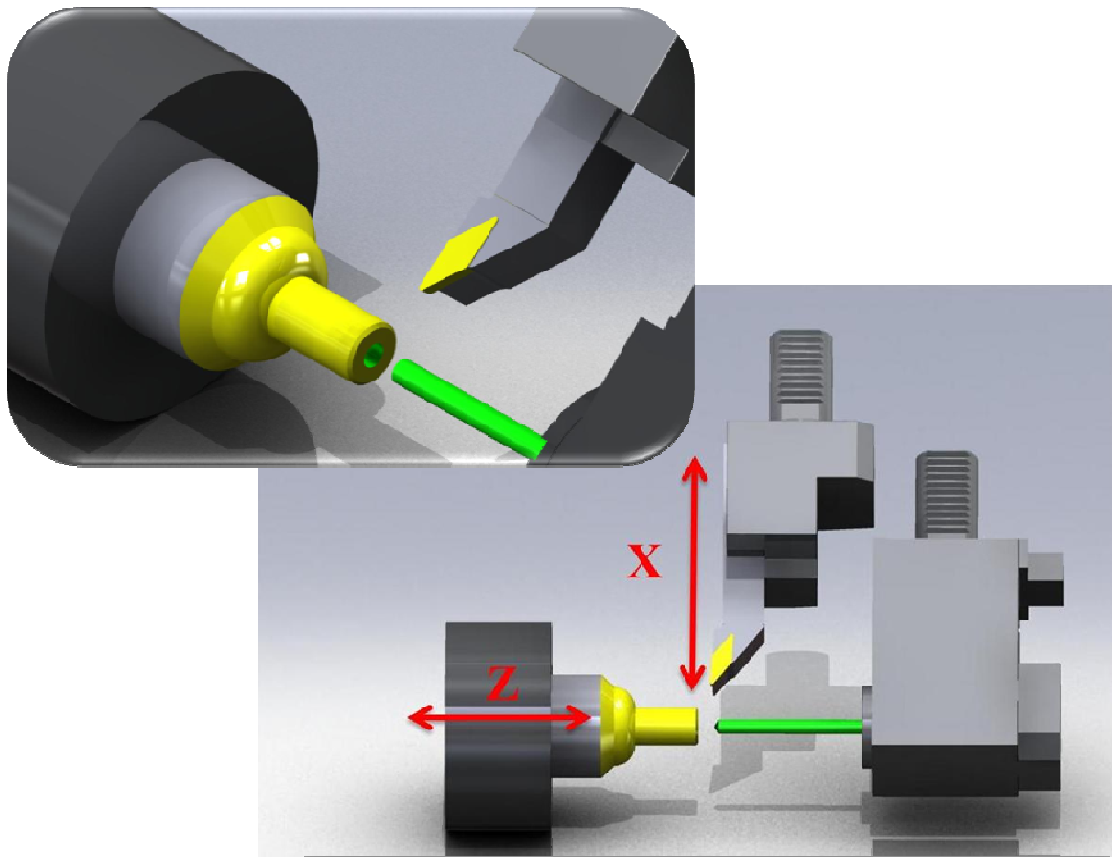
rotierende Spindel und stillstehende Werkzeuge
